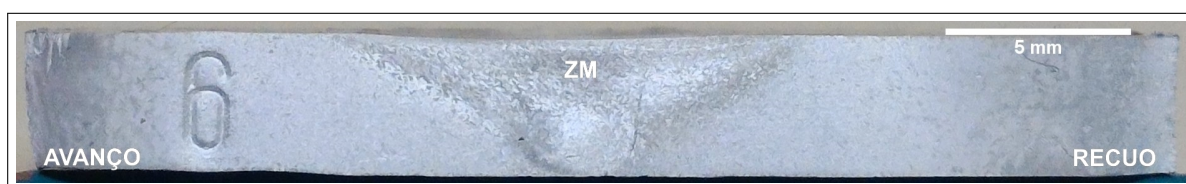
Macrografia de amostra soldada a 1500 rpm e 50 mm/min
